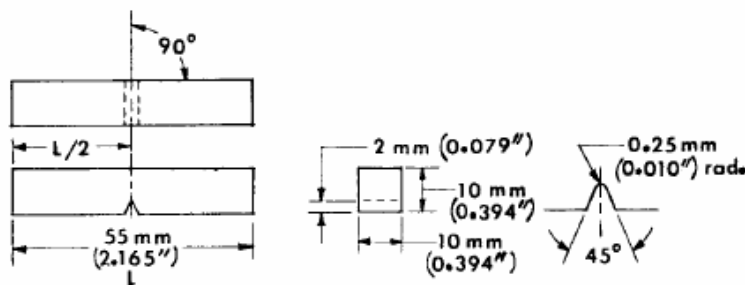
Medidas padrões do corpo-de-prova para Ensaio Charpy
